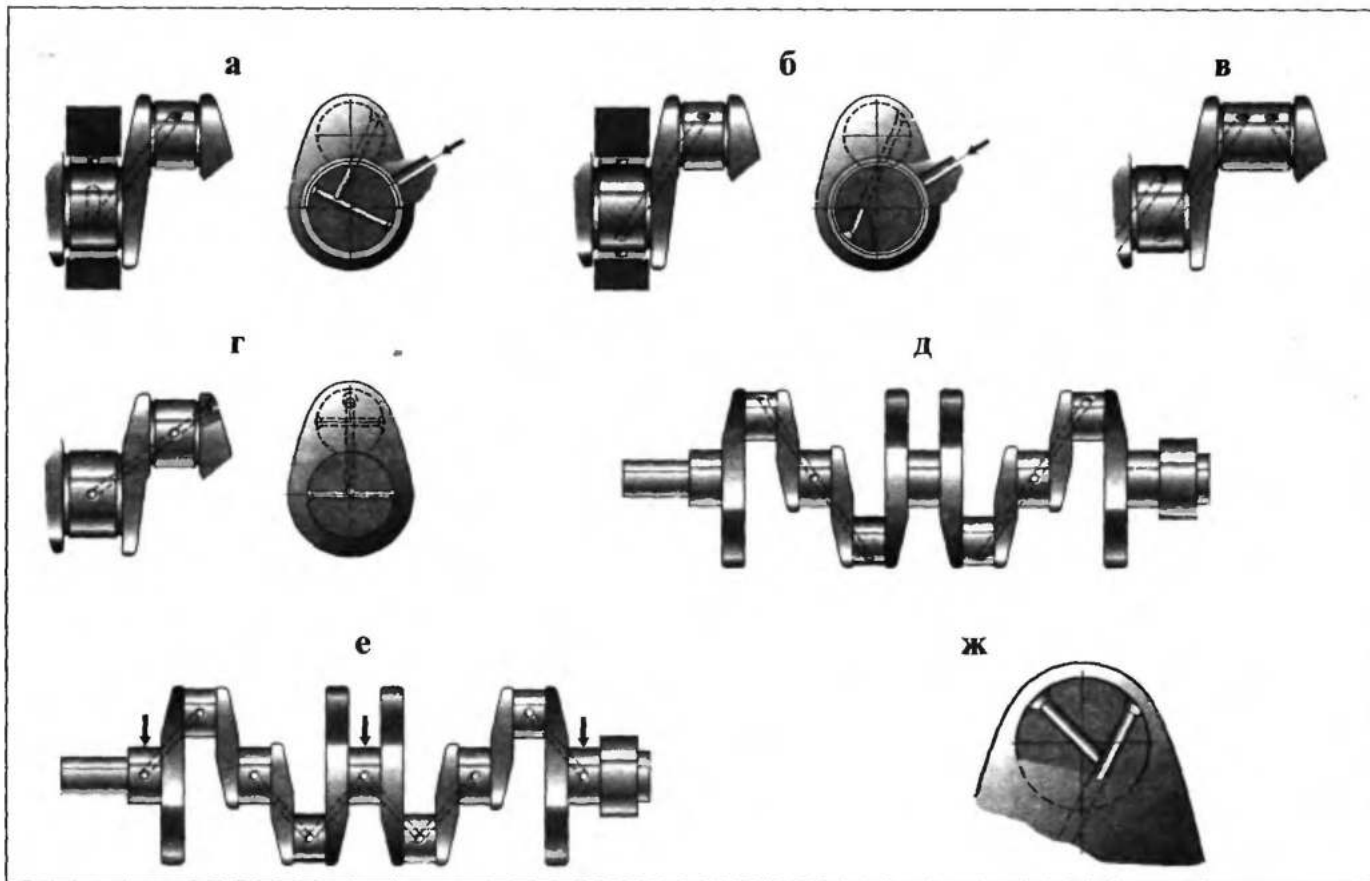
Схемы смазки шатунных подшипников коленчатого вала:
